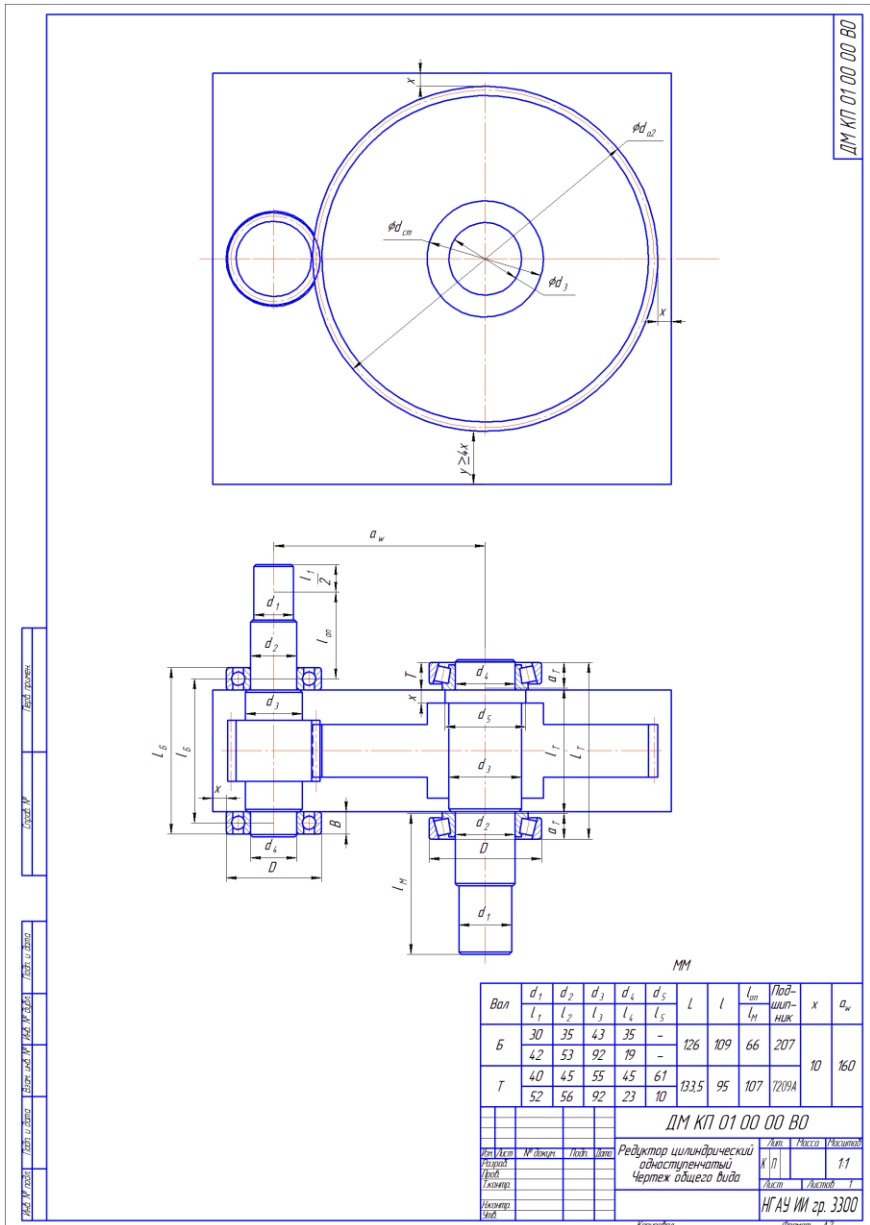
Пример чертежа общего вида цилиндрического одноступенчатого редуктора
